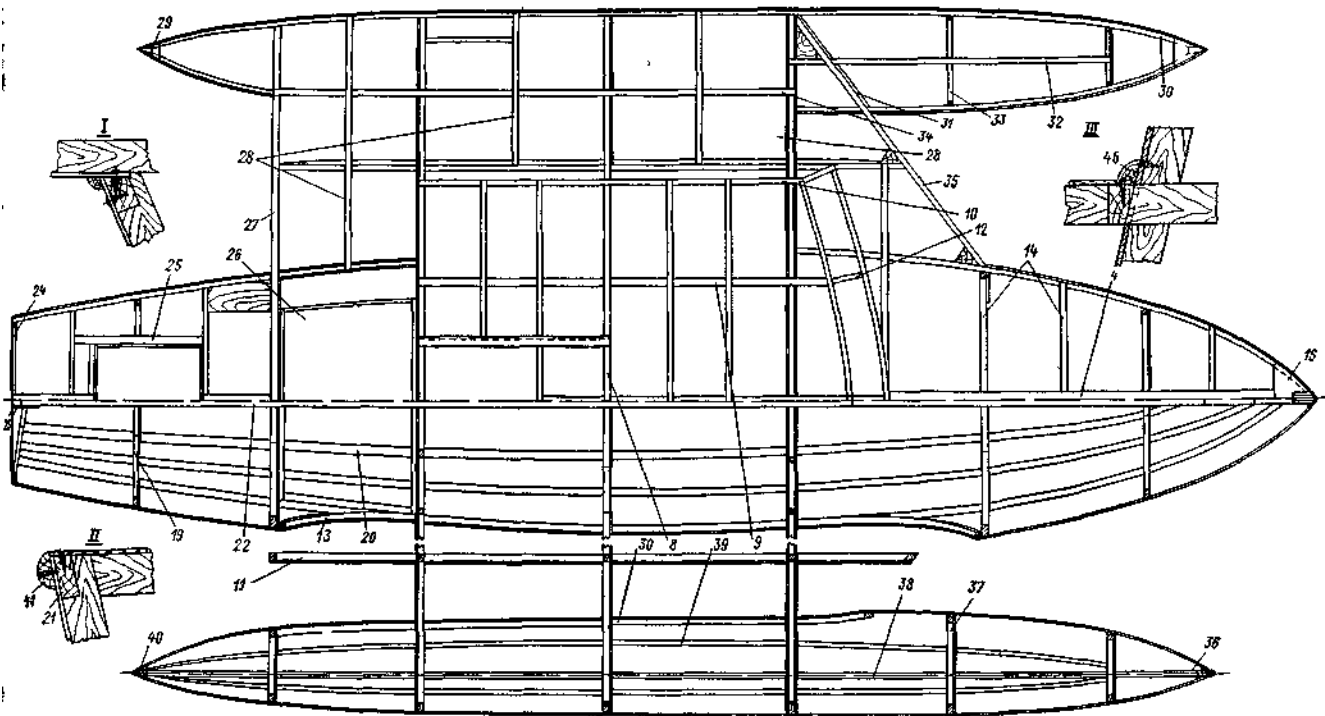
Конструктивный чертеж и сечения по шпангоутам.
